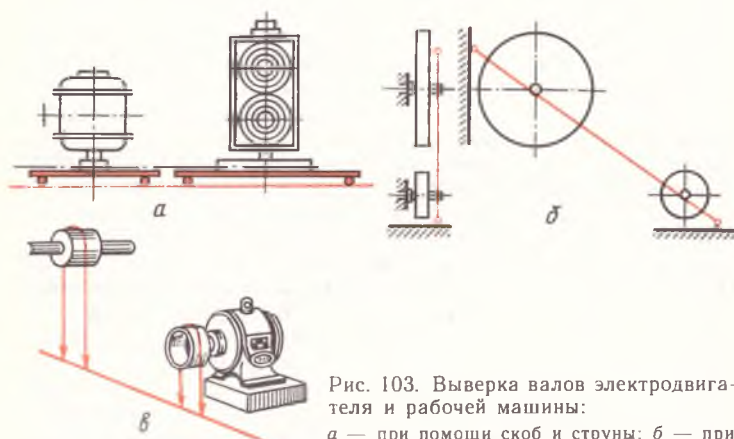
Выверка валов электродвигателя и рабочей машины:
